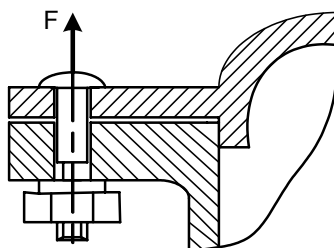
Винт (шпилька) установлен в отверстие несущей конструкции (например, для соединения крышки с корпусом и т.п.) и нагружен осевой растягивающей силой F
